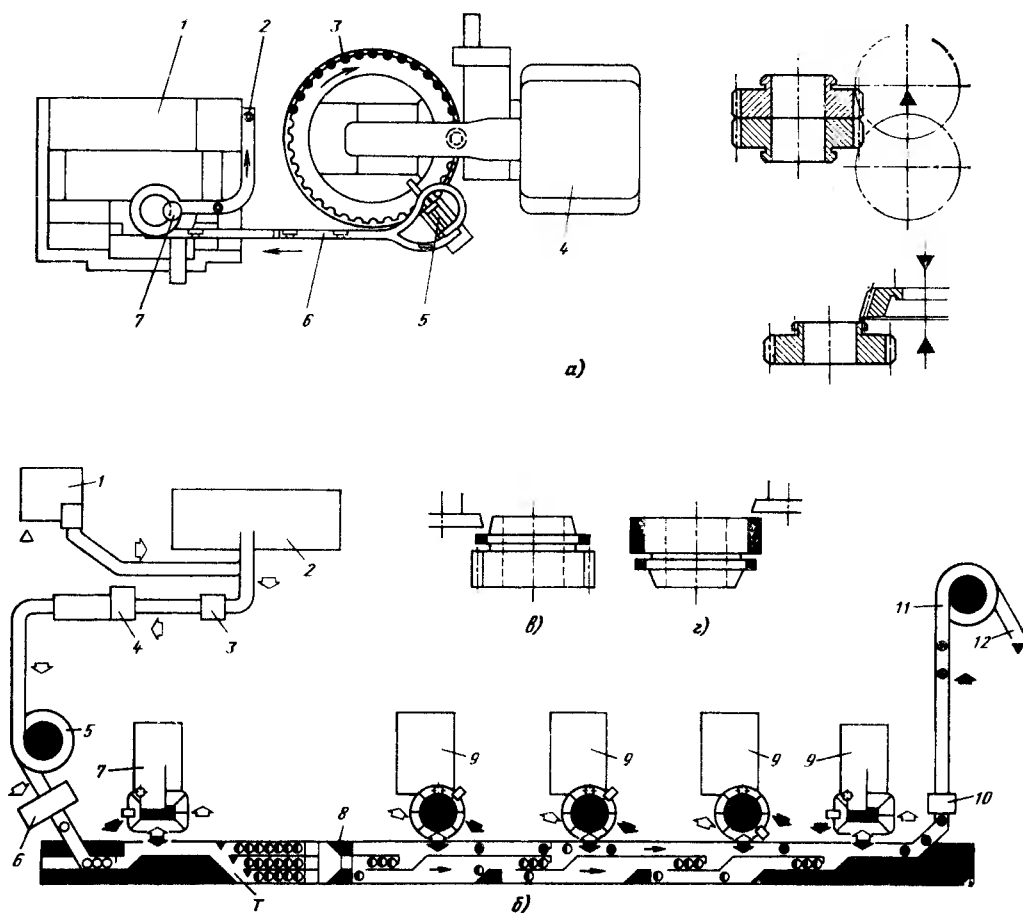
Схема автоматической линии для изготовления цилиндрических зубчатых колес
